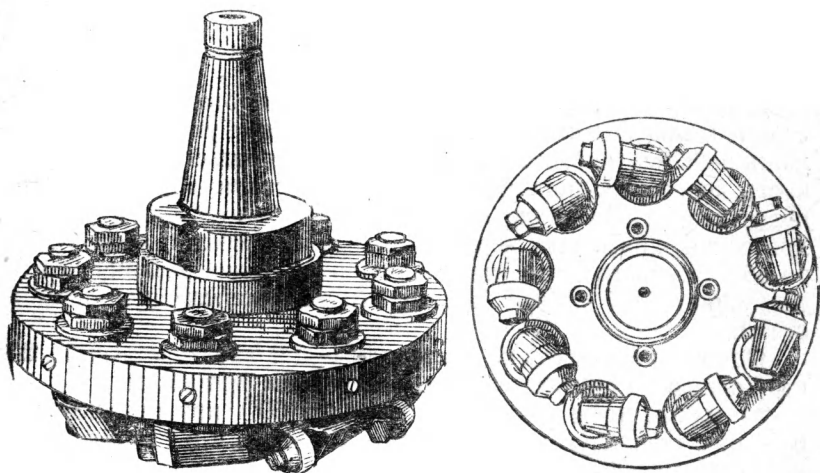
Торцовая фреза с режущими кольцами из керамики.
